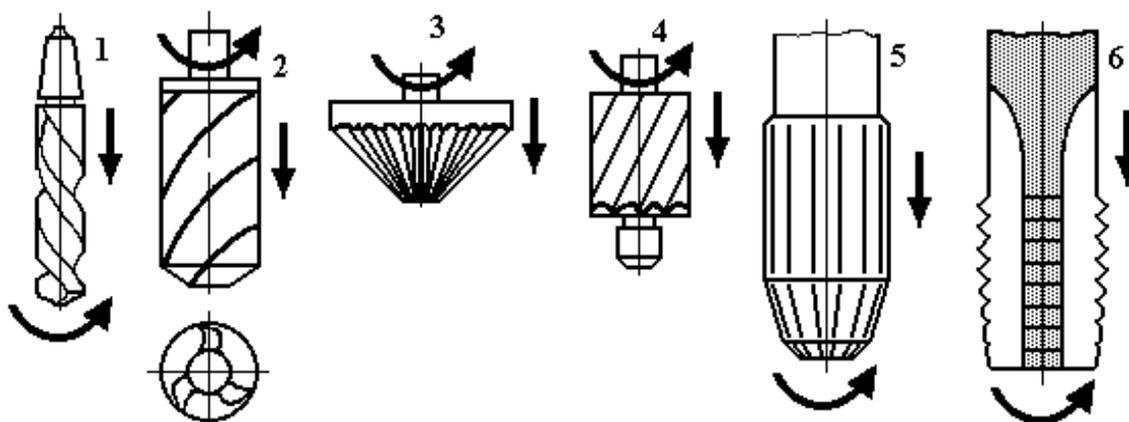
Осевой режущий инструмент: 1 – сверло спиральное; 2 – зенкер цилиндрический спиральный; 3 – зенкер конический; 4 – зенкер торцовый с направляющей цапфой; 5 – развертка цилиндрическая; 6 – метчик
